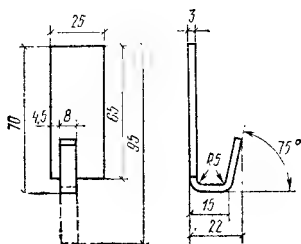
Крючки типа 23кс (масса 0,039 кг) для крепления высоко располагаемых смывных бачков на кирпичных или бетонных стенах дюбель-гвоздями
